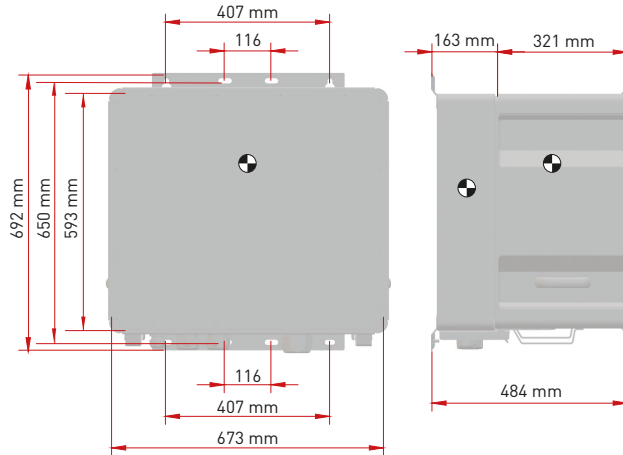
Abmessungen PowerUnit mit ConnectionBox
